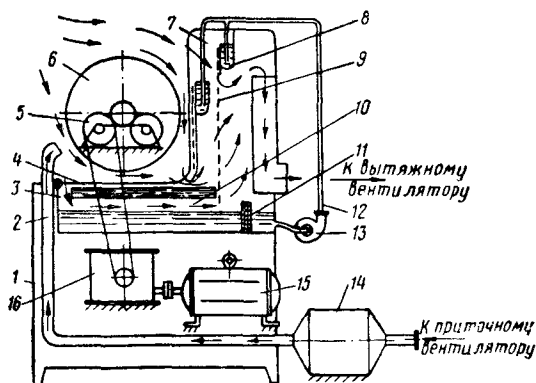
Схема установки для окраски и сушки якорей с системой гидрозащиты:
